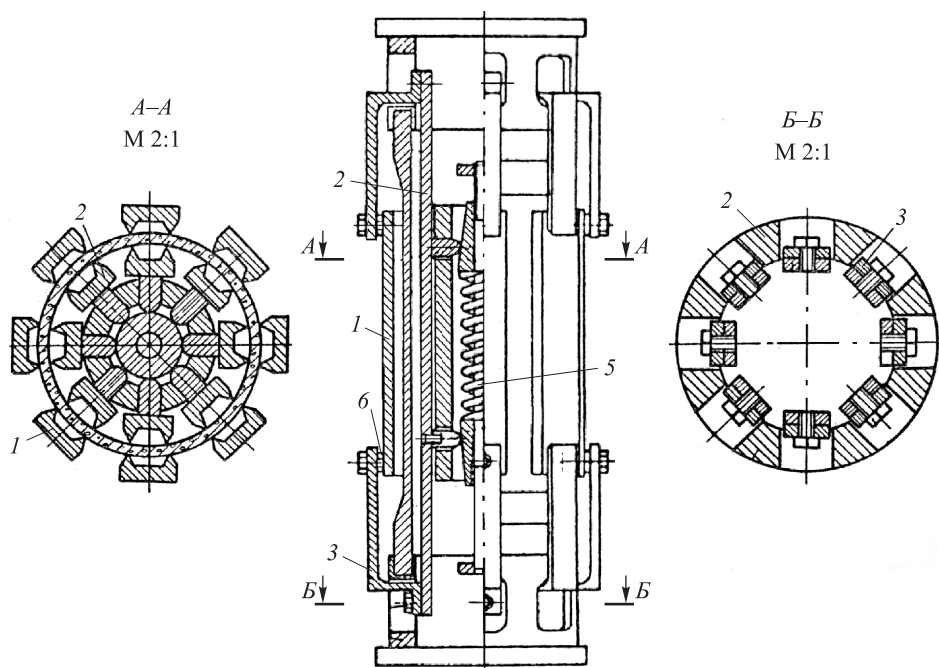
Устройство для испытания цилиндрических образцов КМ с двухсторонними связями (как изнутри, так и снаружи)
